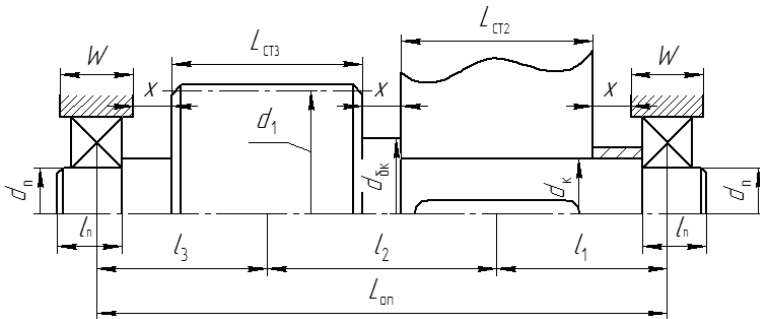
Эскиз промежуточного вала цилиндрического двухступенчатого редуктора
